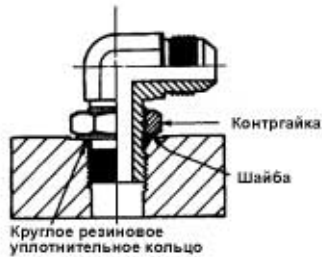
Угольник с цилиндрической резьбой и уплотнительным кольцом
